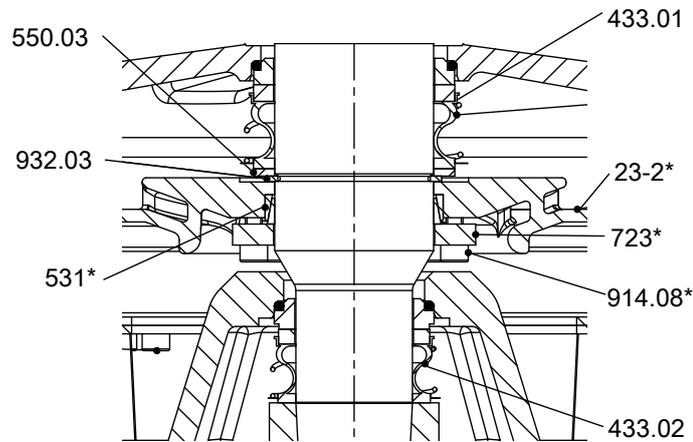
Cierre mecánico para motores: 35 4...110 4, 32 6...100 6, 26 8...75 8
